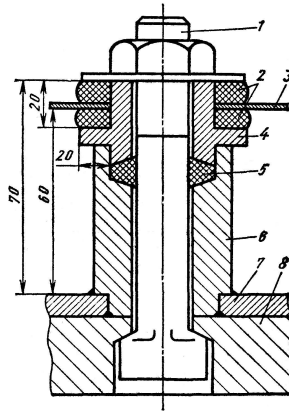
Узел крепления оболочки к корпусу барабана:
